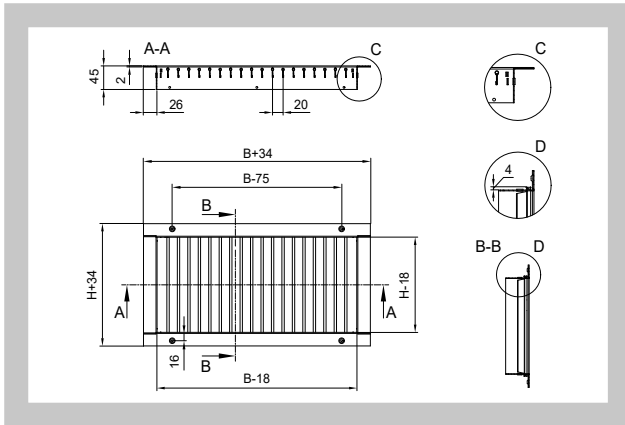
Einstellbare Lamellen vertikal - einreihig B > 750 mm
